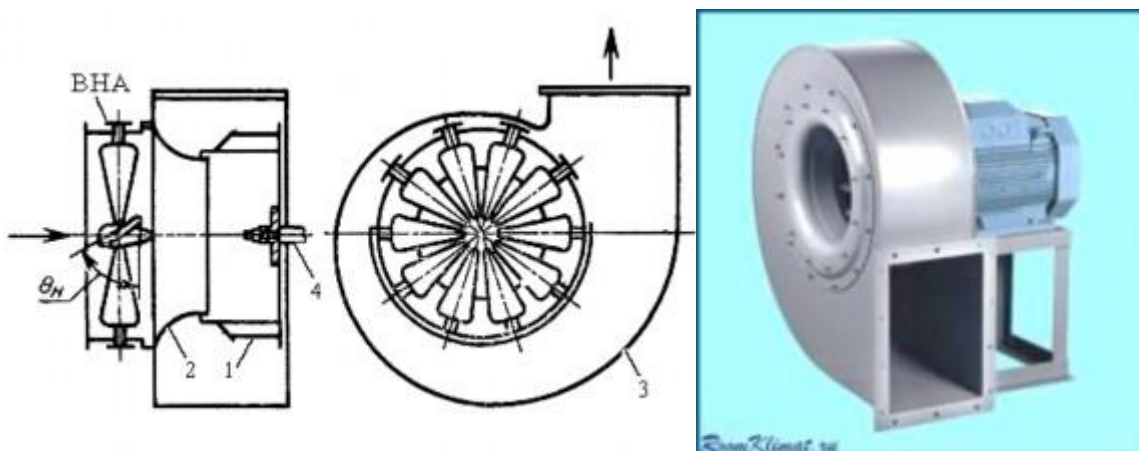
Общий вид и конструктивная схема одноколесного центробежного вентилятора:
